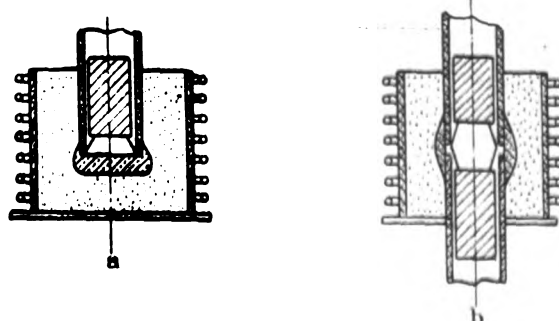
Schémas de constitution ou de modification de pièces de silice par le chauffage par induction à haute fréquence : a, soudure d'un fond à un tube; b, soudure de deux pièces bout à bout.
